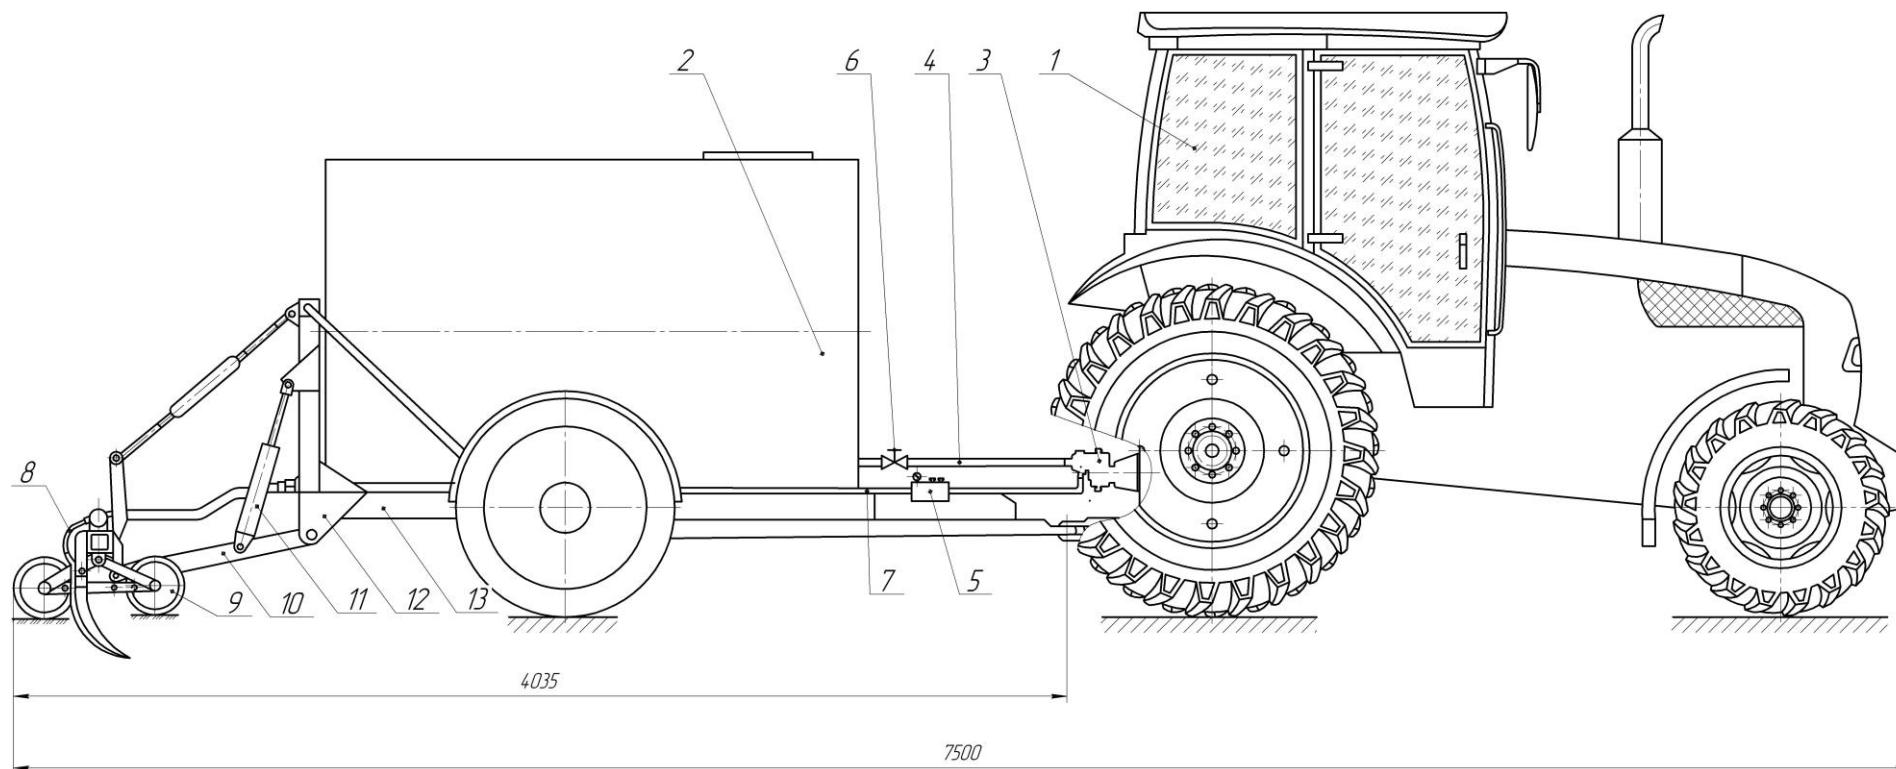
Конструктивна схема агрегату для внесення КАС:
